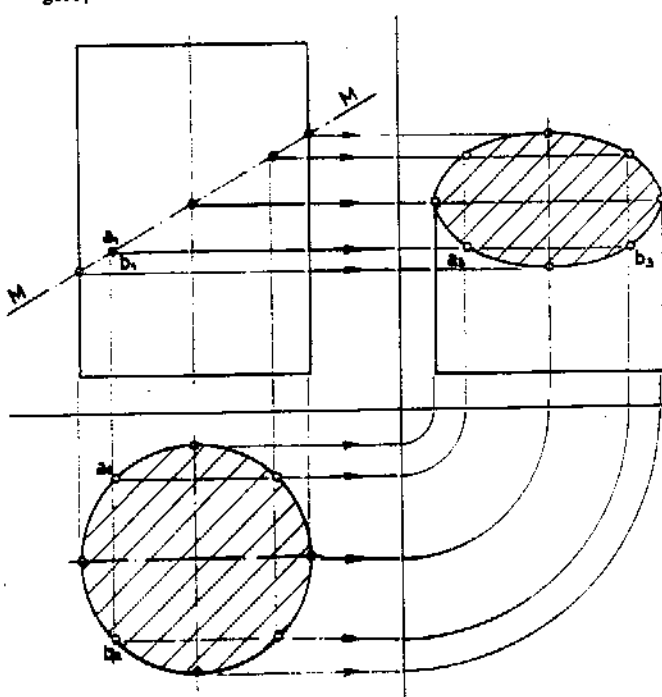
Sezione di un cilindro mediante un piano di traccia MM ortogonale rispetto al P.V. e inclinato sul P.O. La sezione sul P.L. risulta una ellisse.
